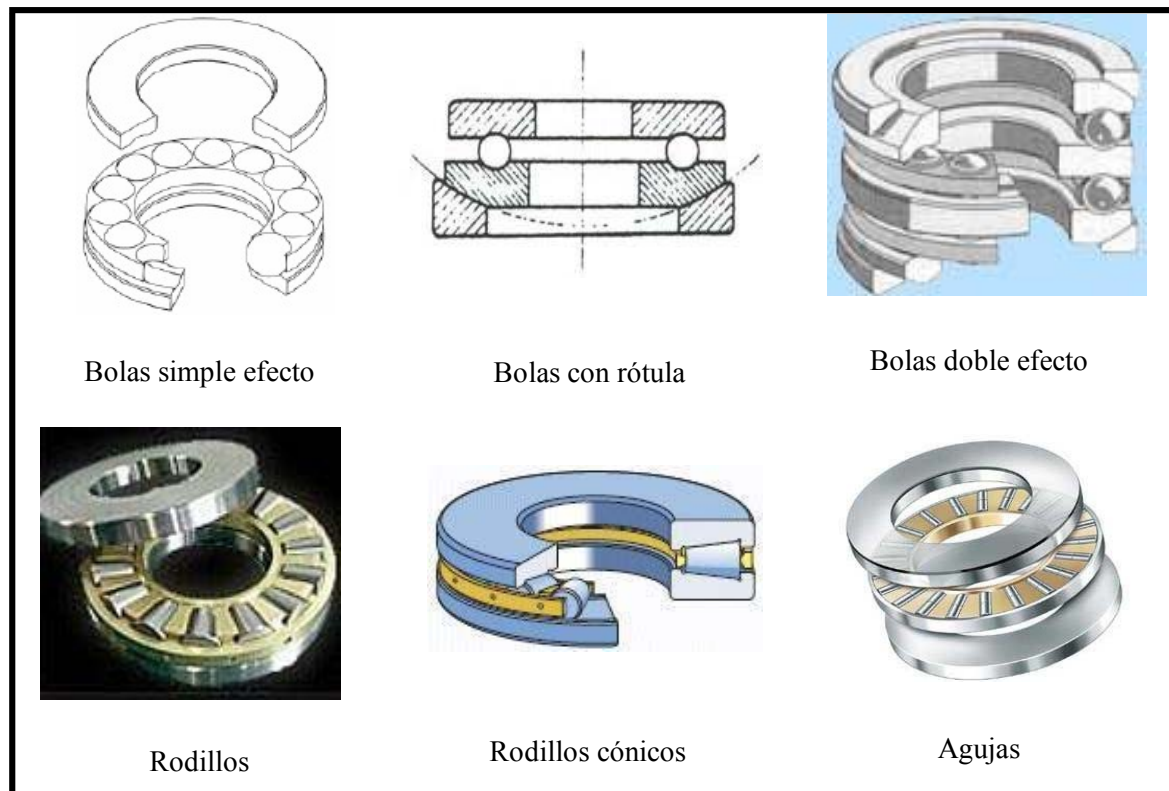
Tipos de rodamientos axiales. [P4]
